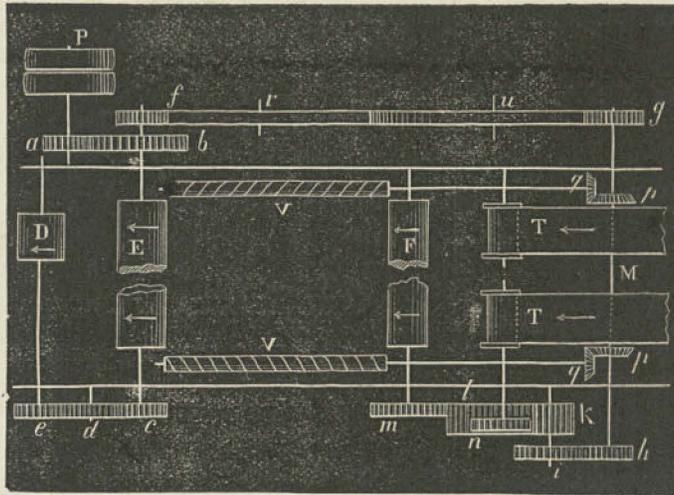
Projection d'une table à étaler. — Vue de dessus.
